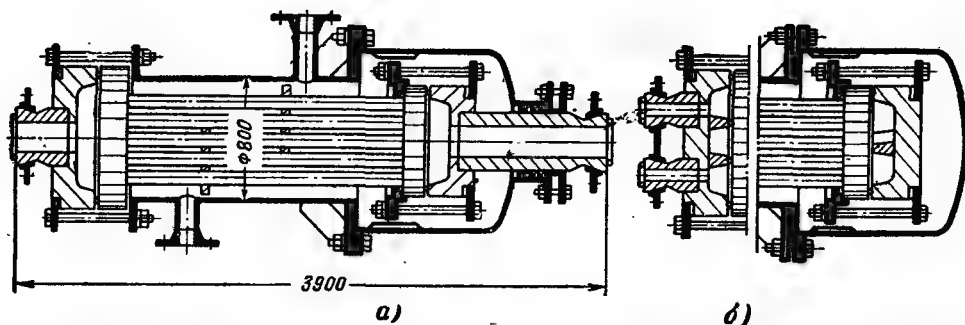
Кожухотрубный графитный теплообменник со стальным кожухом и плавающей головкой.
